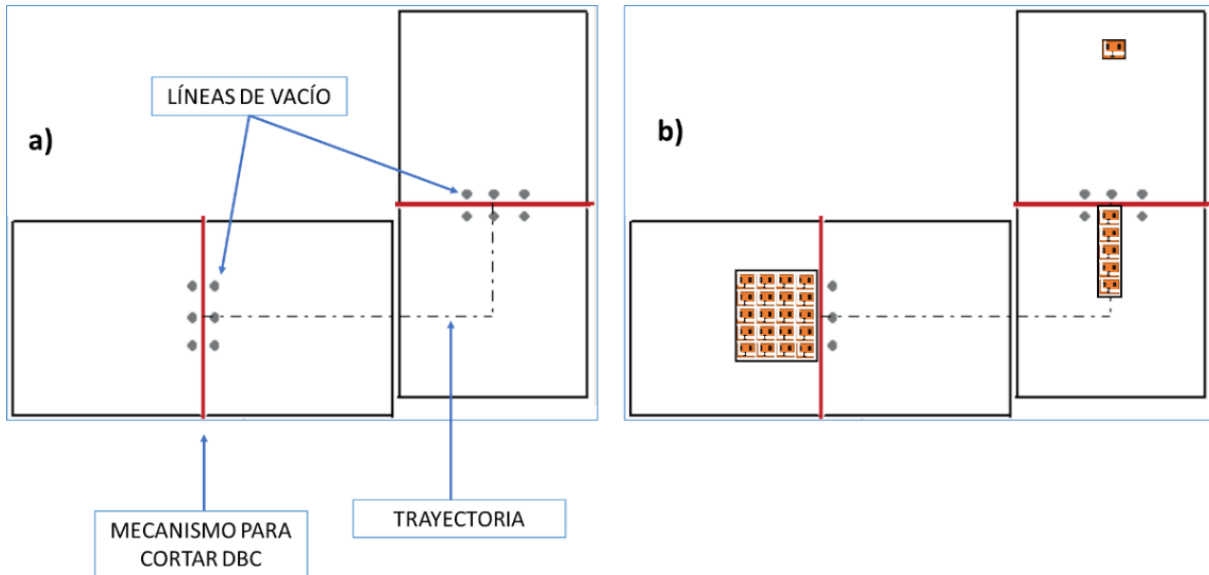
a) Layout de la mesa de corte b) Proceso de corte a lo largo de toda la mesa de corte
